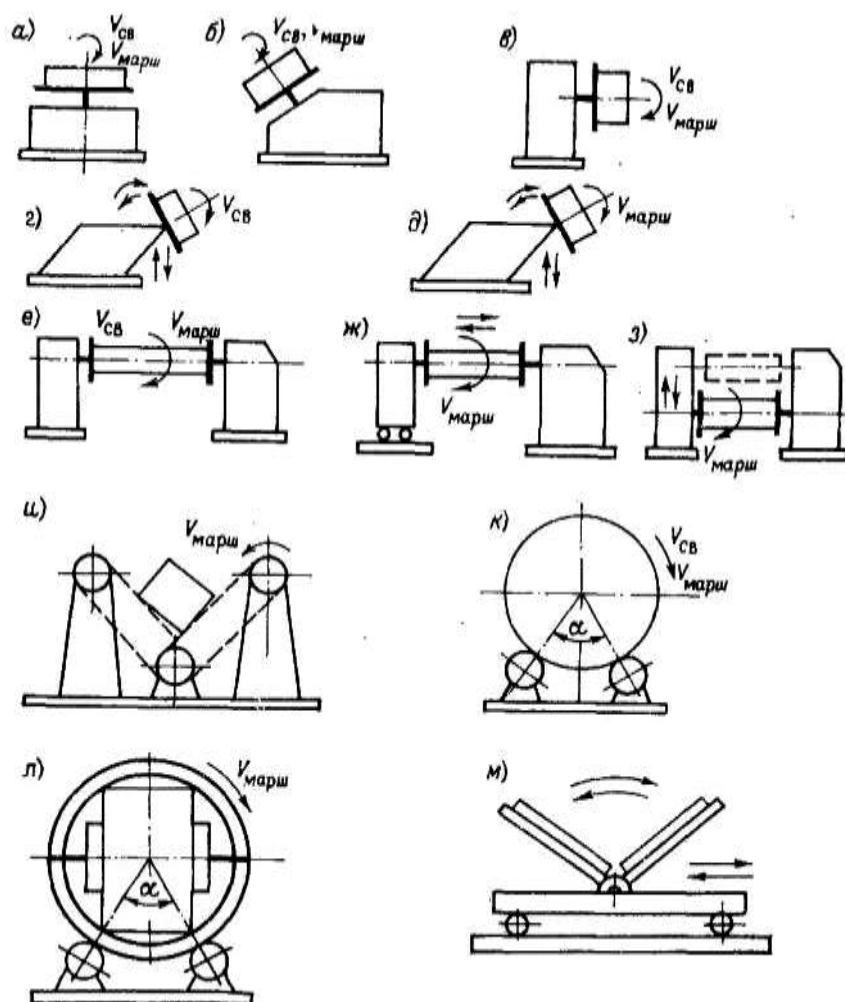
Схемы кантователей для сварки изделий:
